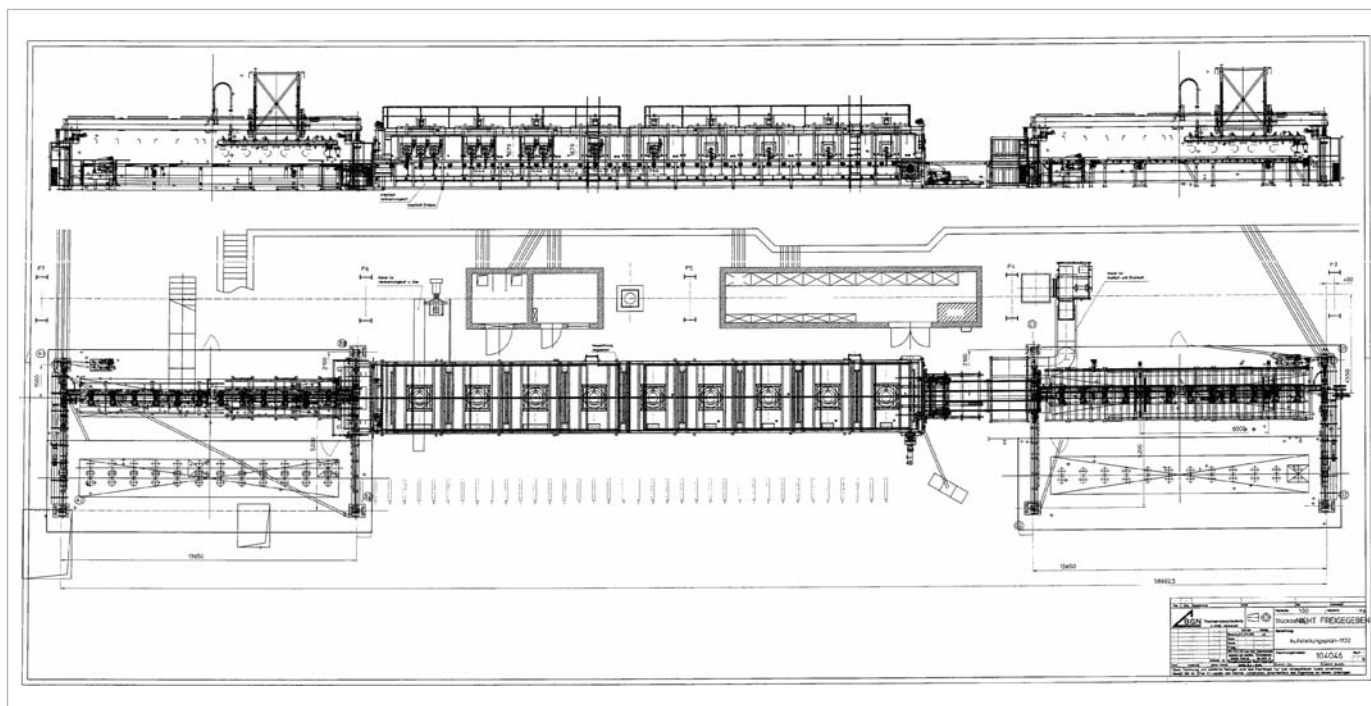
Layout einer kompletten Banddurchlauf-Ofenanlage
